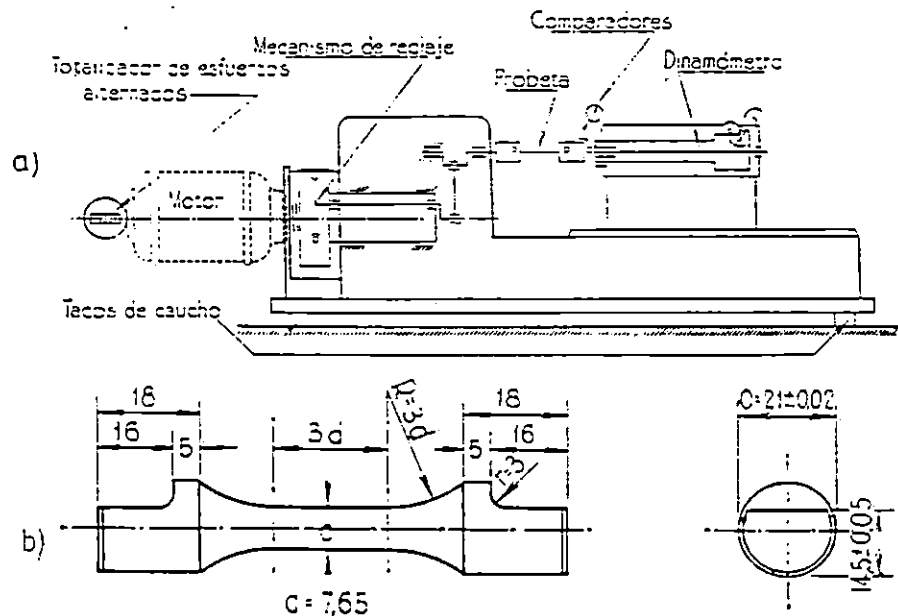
Máquina Torsional Alternada Schenck-Erlinger a) Esquema b) Probeta.
